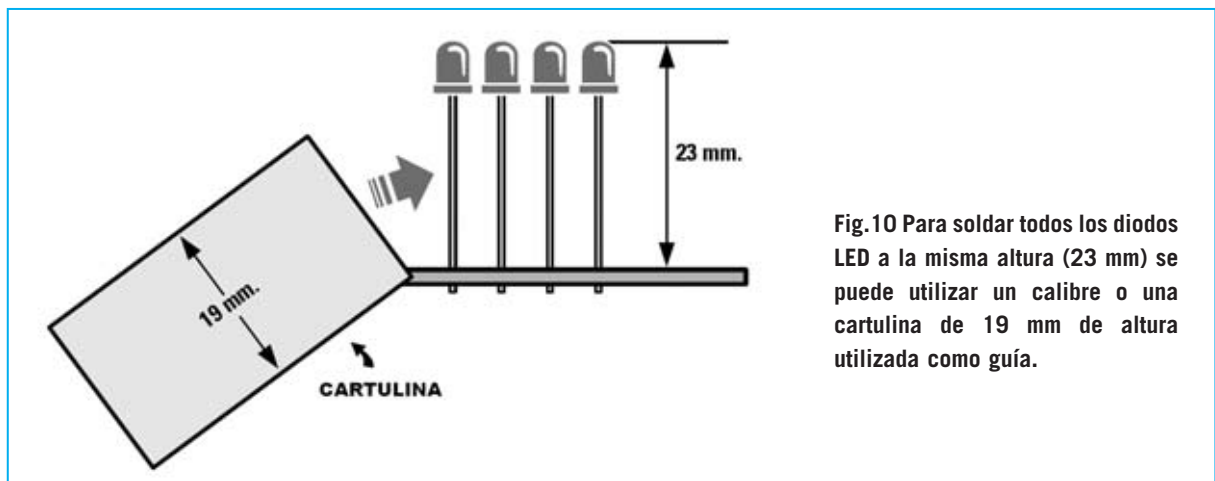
Para soldar todos los diodos LED a la misma altura (23 mm) se puede utilizar un calibre o una cartulina de 19 mm de altura utilizada como guía.
